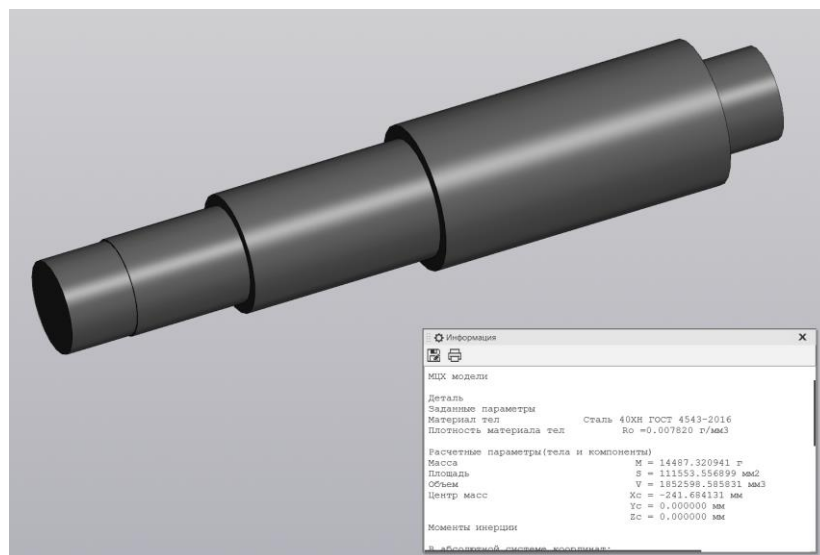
3D модель заготовки виготовленої на ГKM
